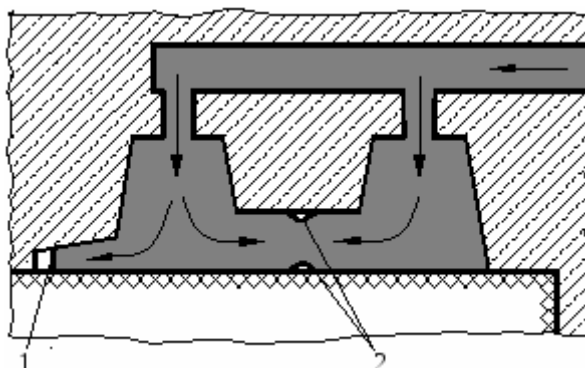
Дефекты отливки в виде недолива 1 и спая 2
